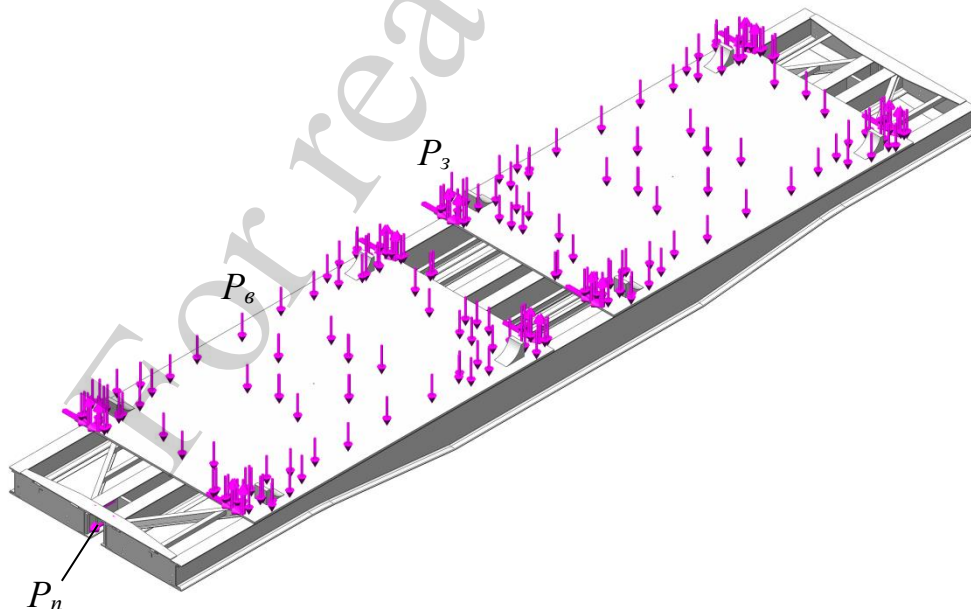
Розрахункова схема несучої конструкції вагона-платформи
